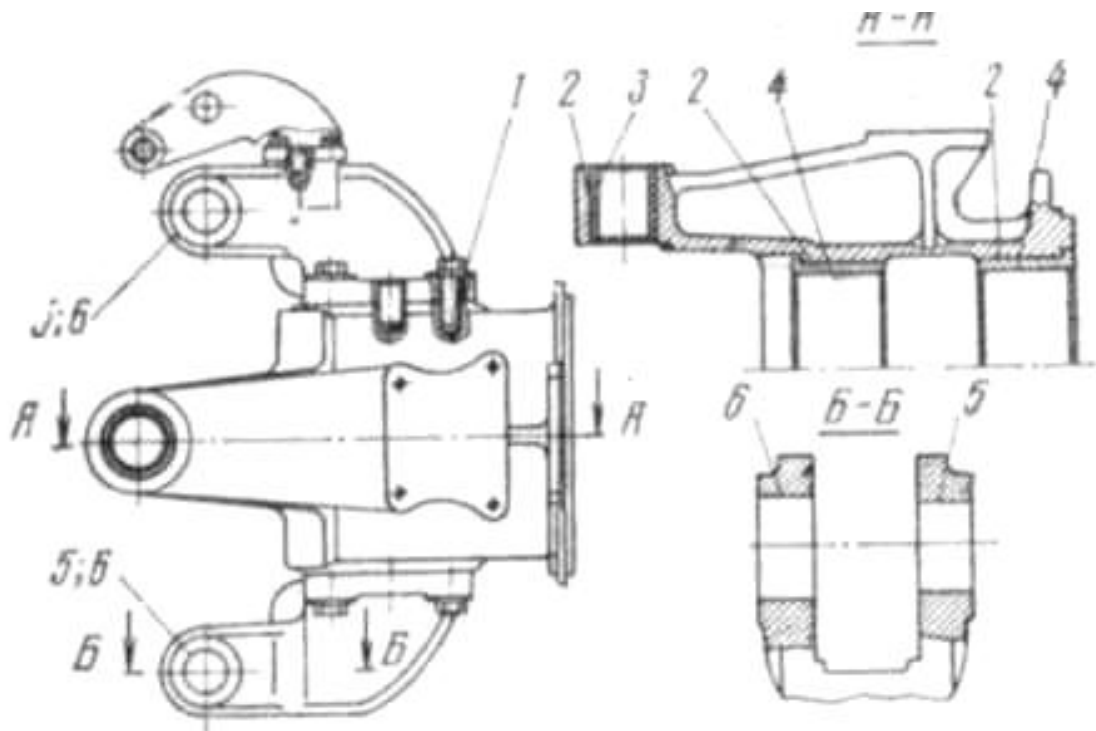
Корпус шарніра 150К.30.018-3СБ
